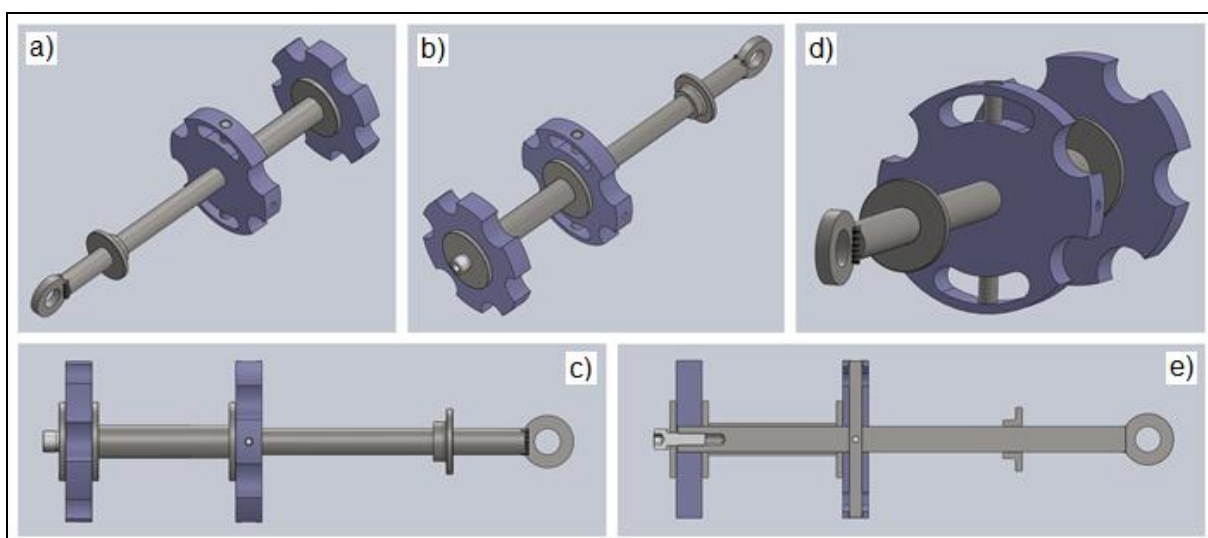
Závěsný trn s pružným zemnicím mechanismem – maskování vodiče.
